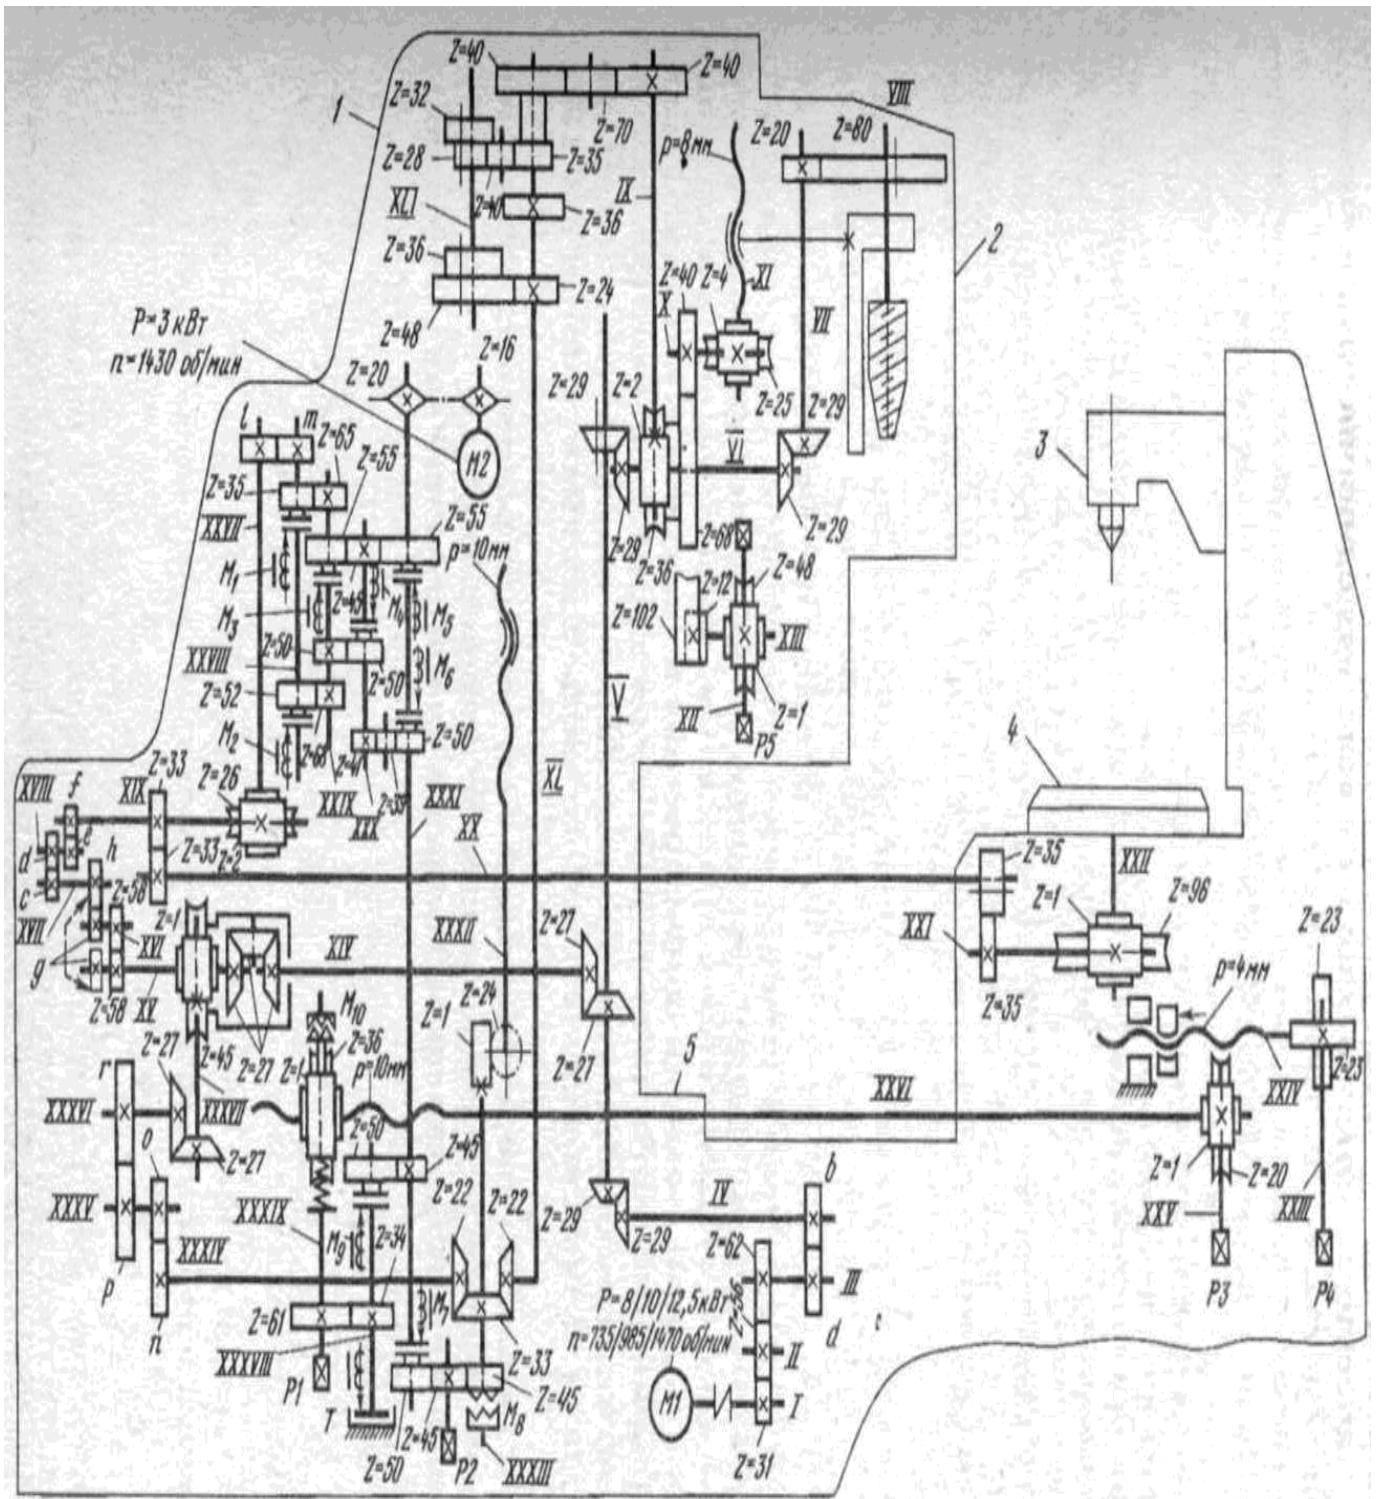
Кинематическая схема зубофрезерного станка модели 53A50.
